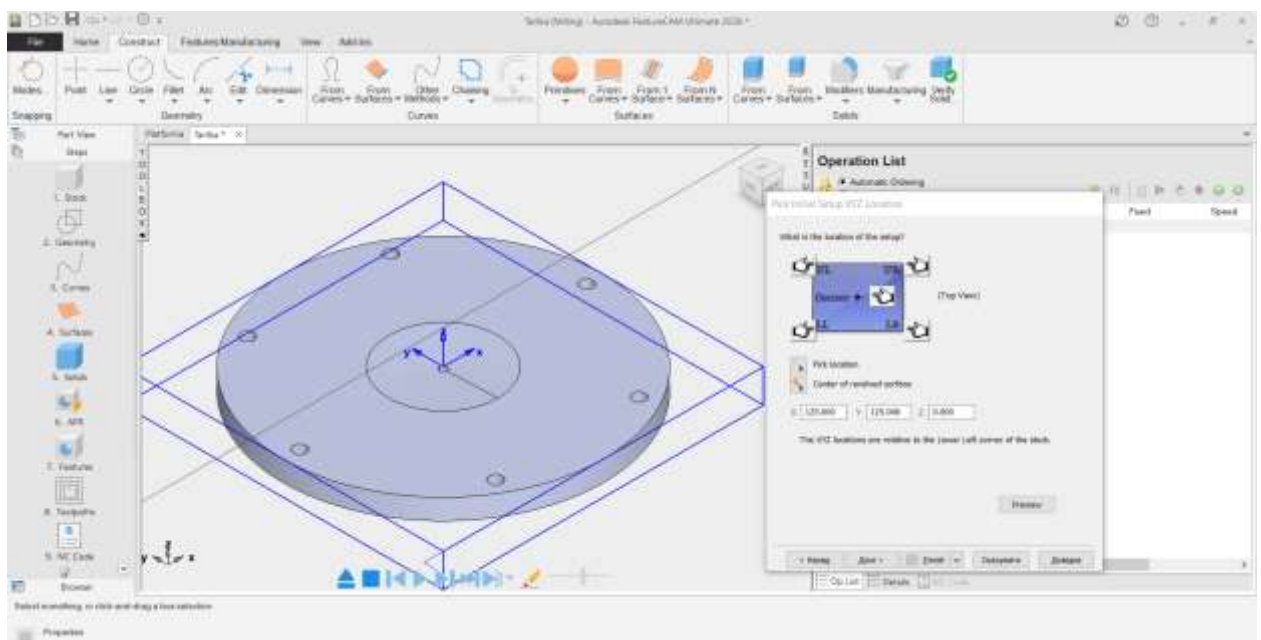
Призначення початкового місця розташування інструменту
